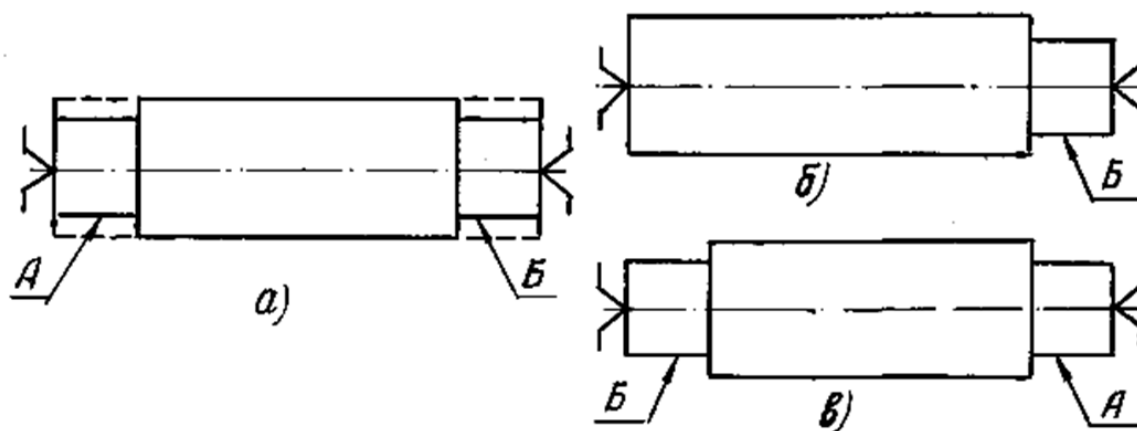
Обработка вала: а) вид заготовки и окончательно обработанной детали; б) вид заготовки после обработки поверхности Б; в) вид заготовки после обработки поверхности А
